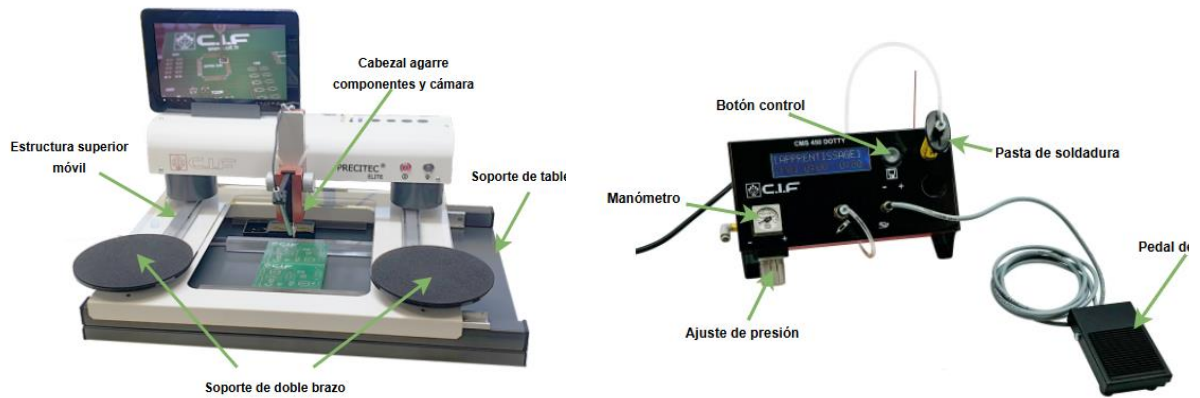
Izquierda Pick and Place y Derecha Dispensador de Pasta a presión.
